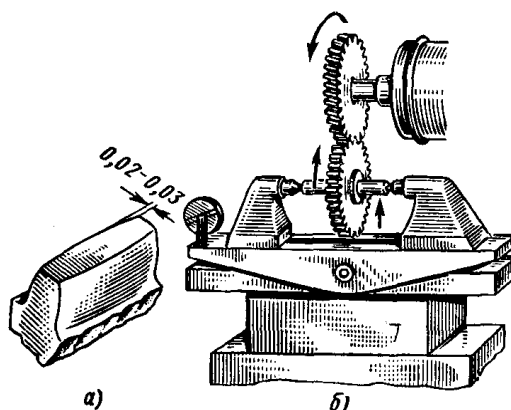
Схема шевінгування бочкоподібного зуба
